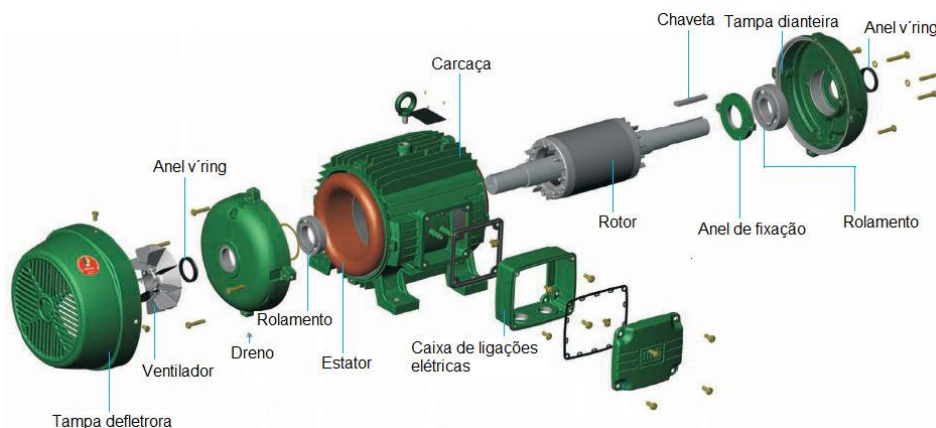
Vista explodida do MIT com rotor do tipo em gaiola de esquilo [13].
